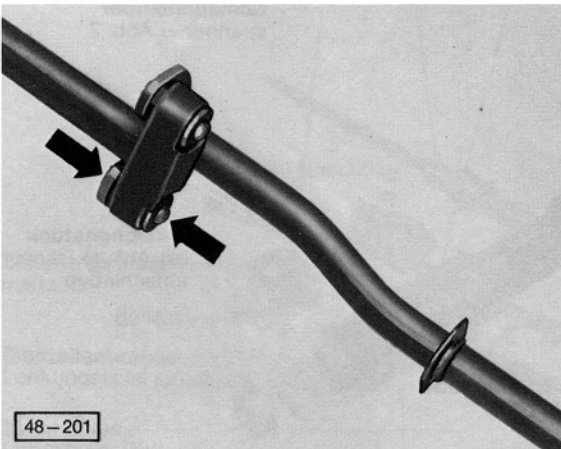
Einbaulage Flanschrohr – Lenksäule
